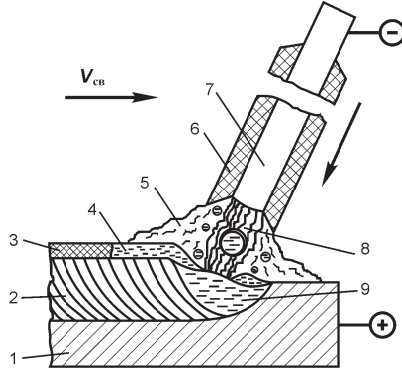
Схема дуговой электросварки металлическим покрытым электродом: 1 – свариваемый металл; 2 – сварной шов (наплавленный металл); 3 – твердая шлаковая корка; 4 – жидкая шлаковая ванна; 5 – газовая защитная атмосфера; 6 – покрытие электрода; 7 – металлический стержень из сварочной проволоки; 8 – электрическая дуга; 9 – металлическая ванна
